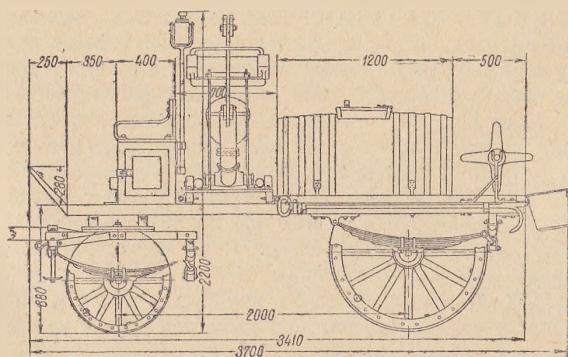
Насосно-бочечный рессорный парокочный ход.
